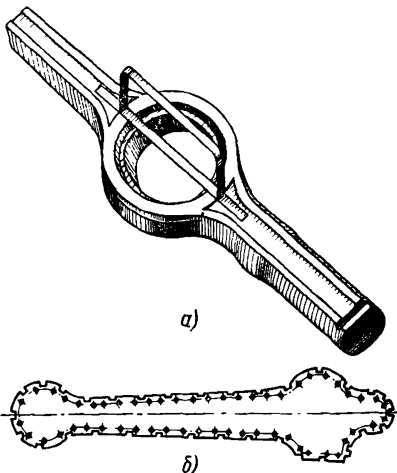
Контурные шаблоны: а — для поковки заднего моста большегрузного автомобиля; б — для проверки припусков по контуру поковки паровозного дышла (отверстия по контуру шаблона служат для целей разметки с помощью кернов)
